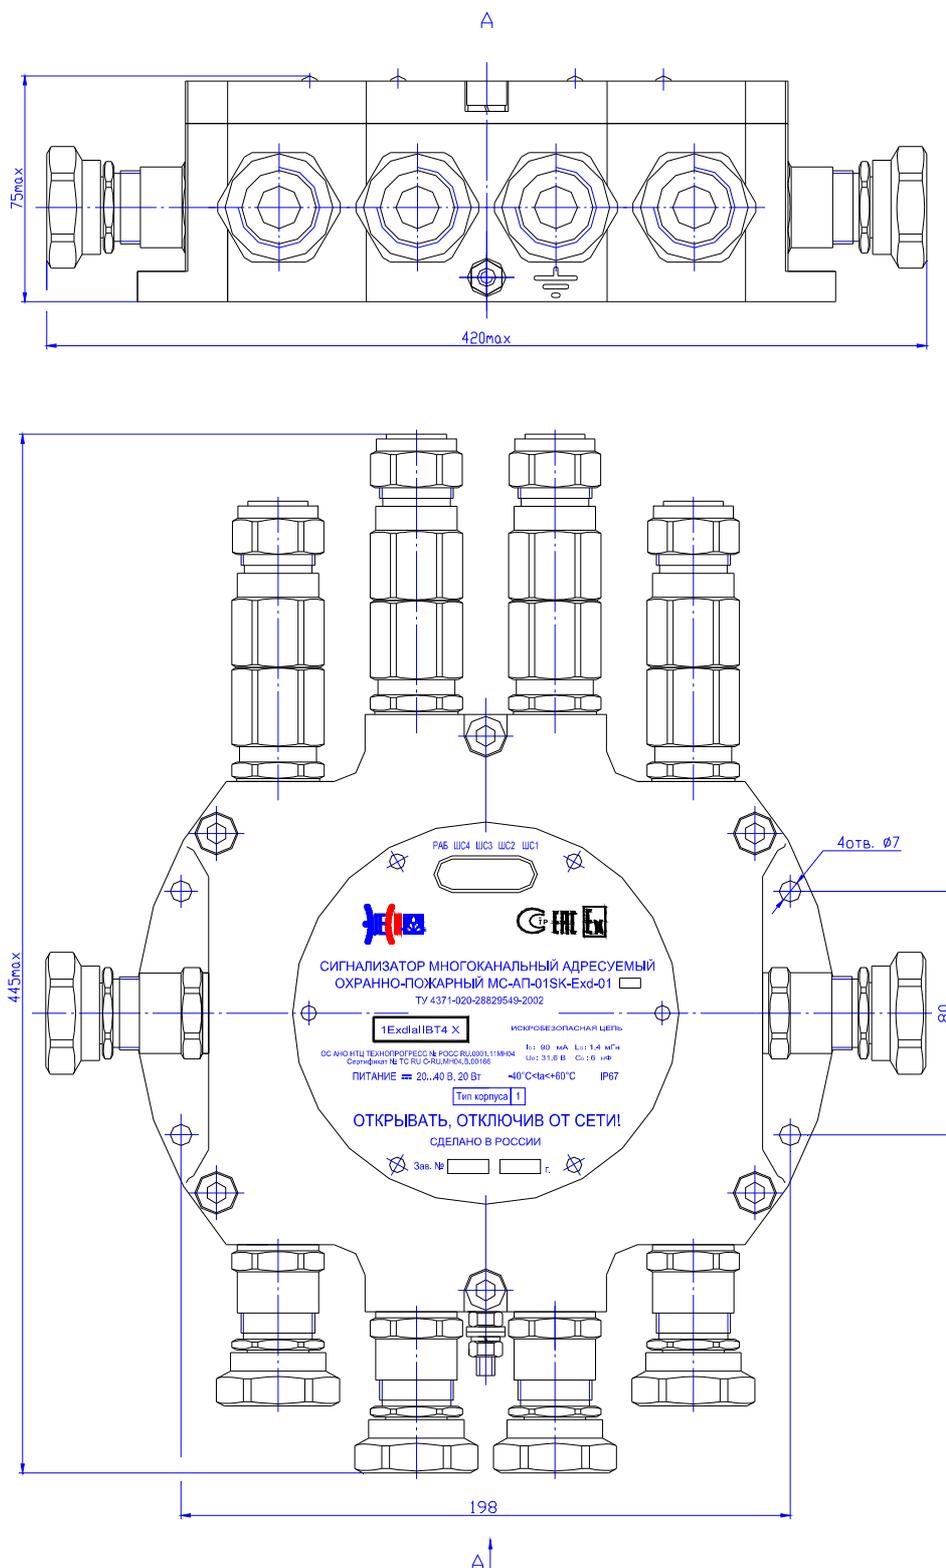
Габаритный чертеж исполнения МС-АП-01СК-Exd
